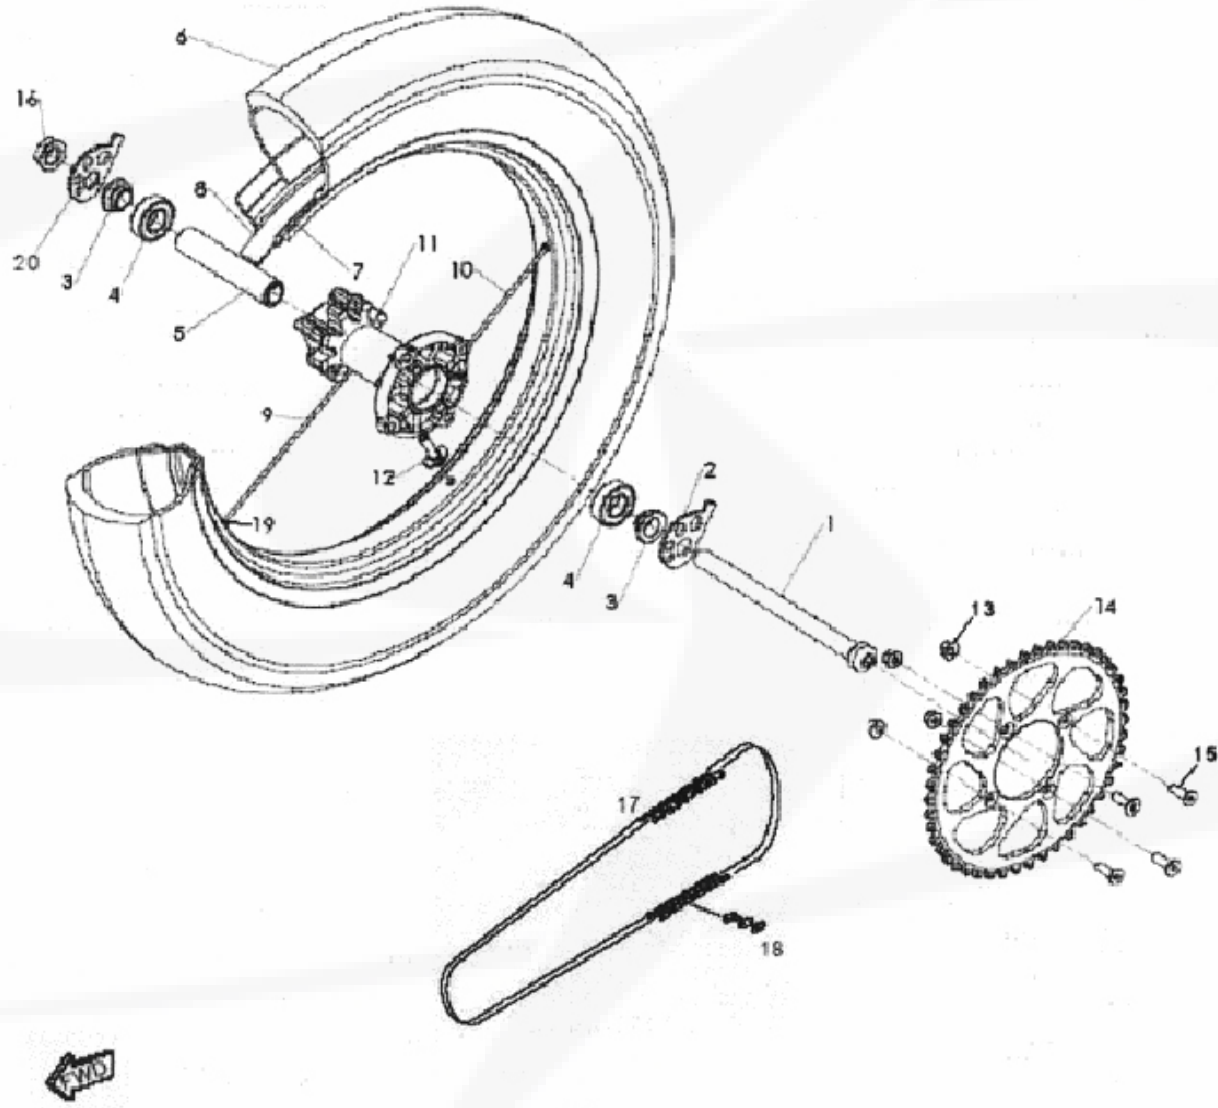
ROUE ARRIÈRE / REAR WHEEL / RUEDA TRASERA
